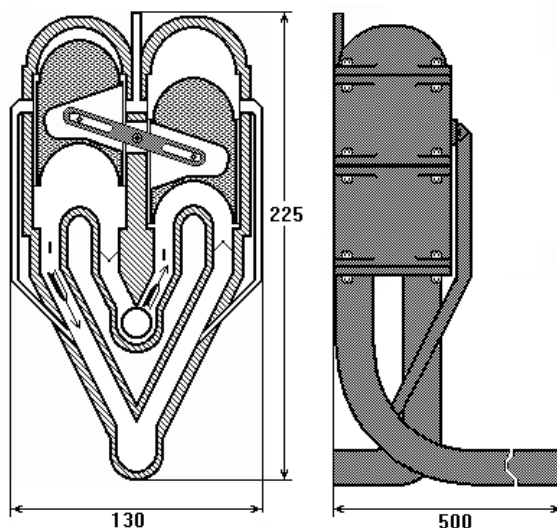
Внешний вид водометного двигателя (слева – сечение)
